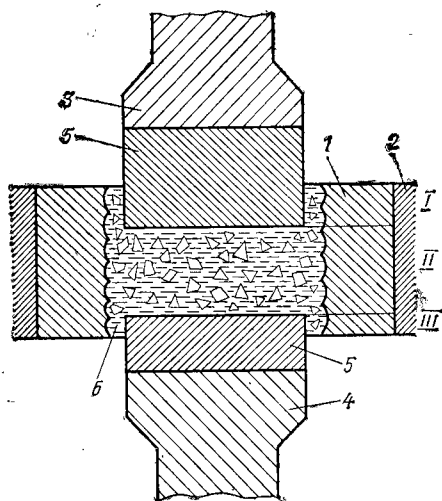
Схема прессования твердосплавной смеси в пресс-форме
